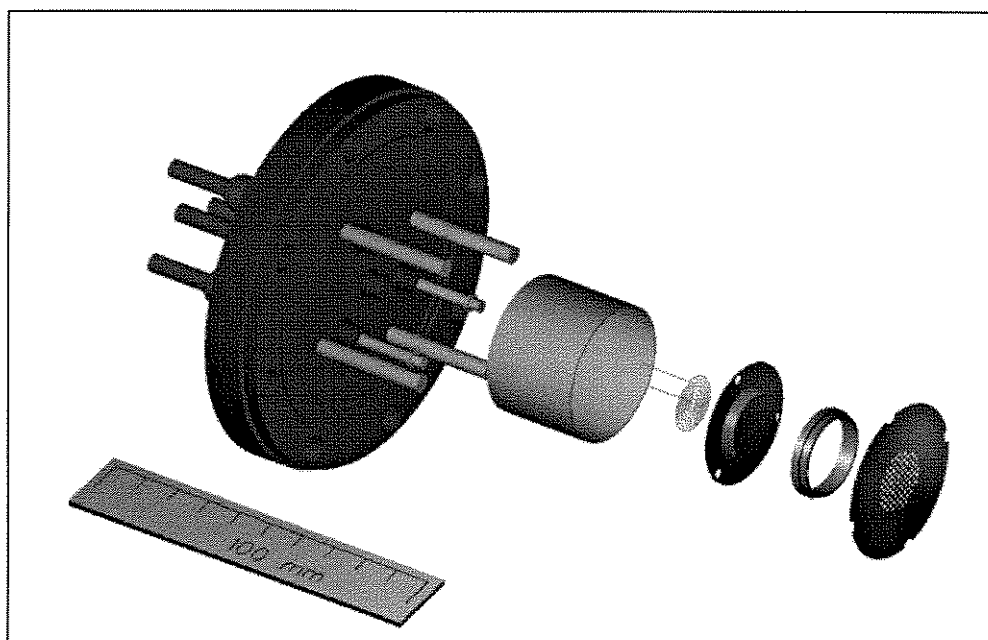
Vista explodida do flange do catodo. Da esquerda para a direita, tem os seguintes elementos: flange de aço inox, blindagem térmica, filamento, catodo de níquel, isolante elétrico cerâmico e grade.
